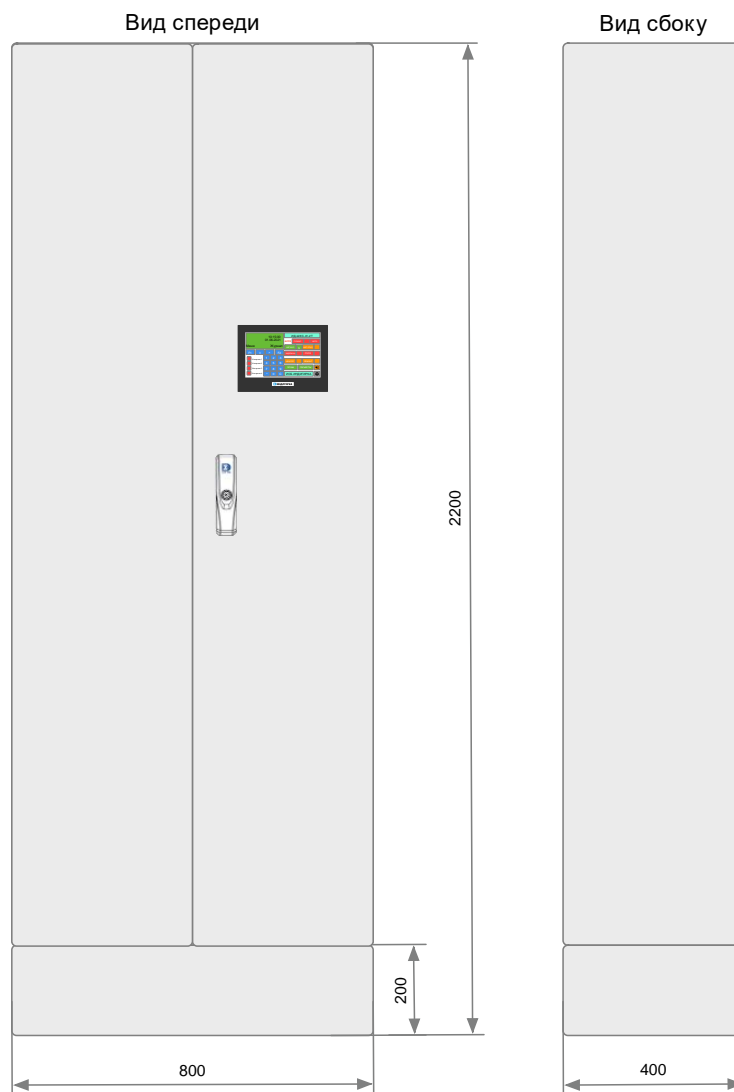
Внешний вид и габаритные размеры концентратора с двухстворчатой дверью
